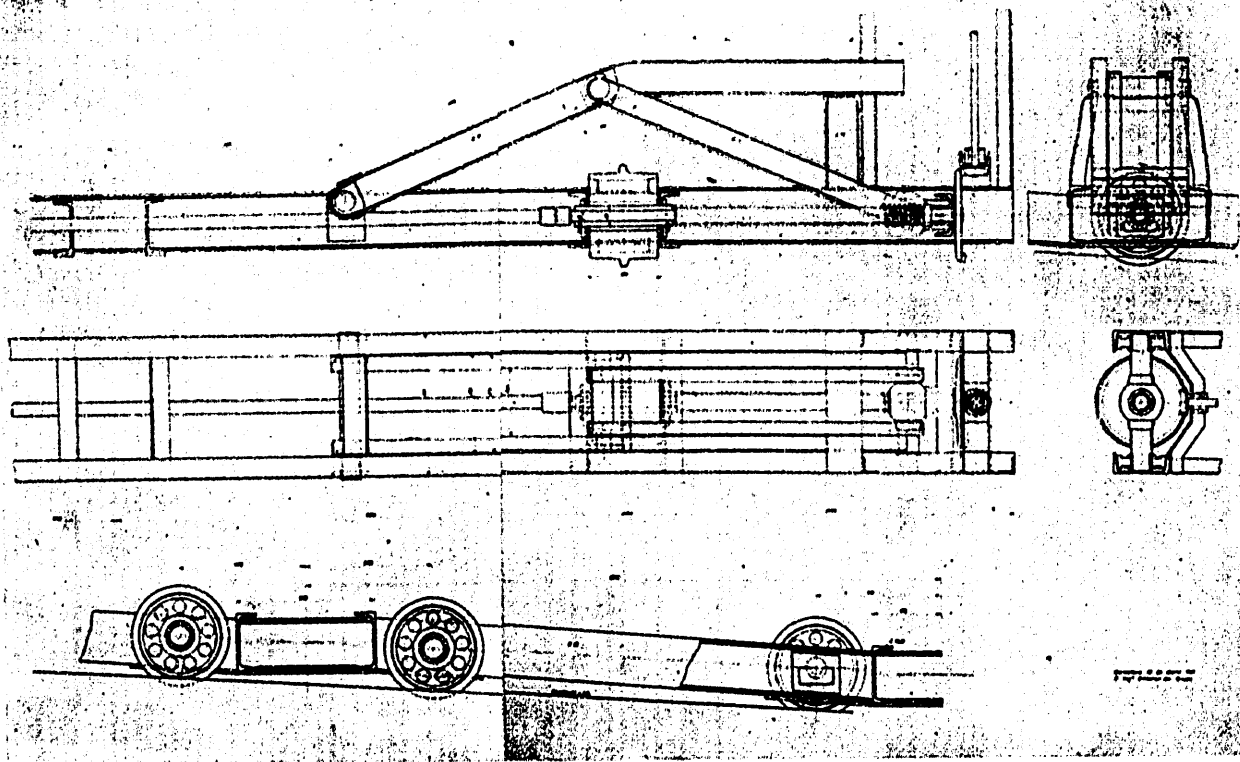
^a — Detalle del sistema de acúñe y de los rodámenes.
